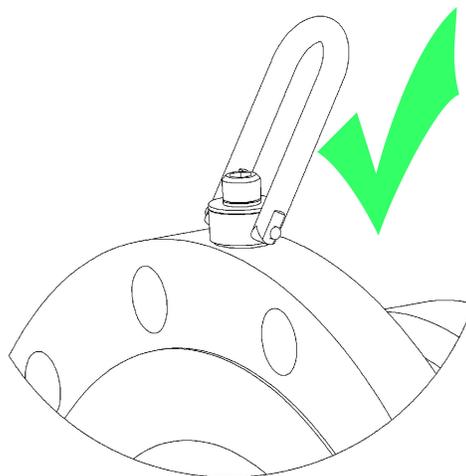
Flange da extremidade do medidor com furo rebaixado plano e rosqueado para olhal de içamento
